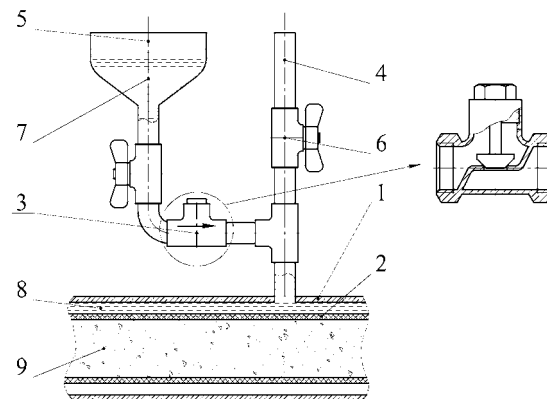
Пристрій для автоматичного поповнення робочої рідини: 1 – корпус гідралічного компенсатора; 2 – трубчаста гумотканнна діафрагма; 3 – зворотний клапан; 4 – трубка для випуску повітря; 5 – місткість для робочої рідини; 6, 7 – шарові крани; 8 – робоча камера компенсатора; 9 – магістраль із розчинною сумішшю
